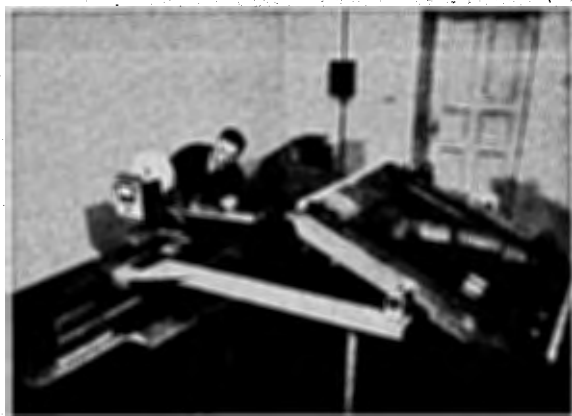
Общий вид намоточного устройства на основе токарно-винторезного станка.
